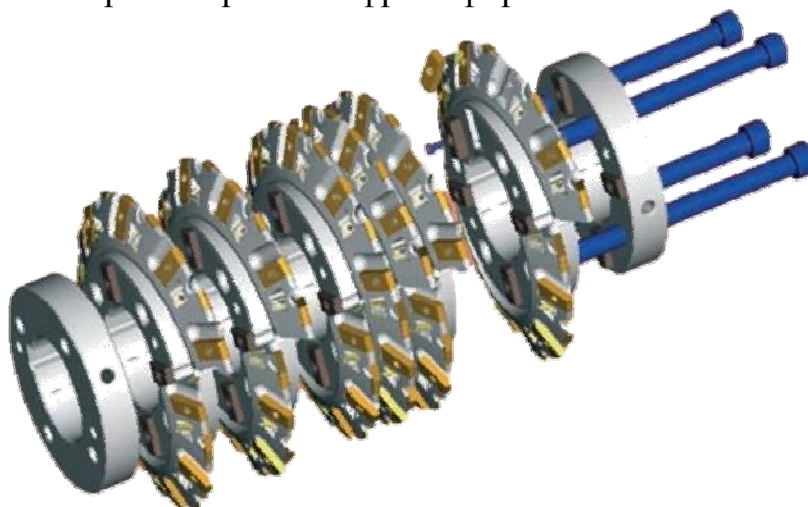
Сборная червячная фреза фирмы «Ingersoll»
